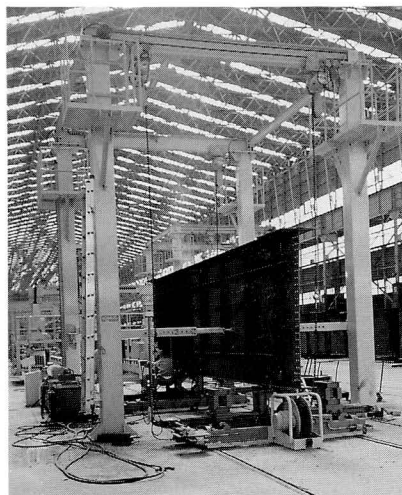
全姿勢溶接反転装置での部材設置状況
